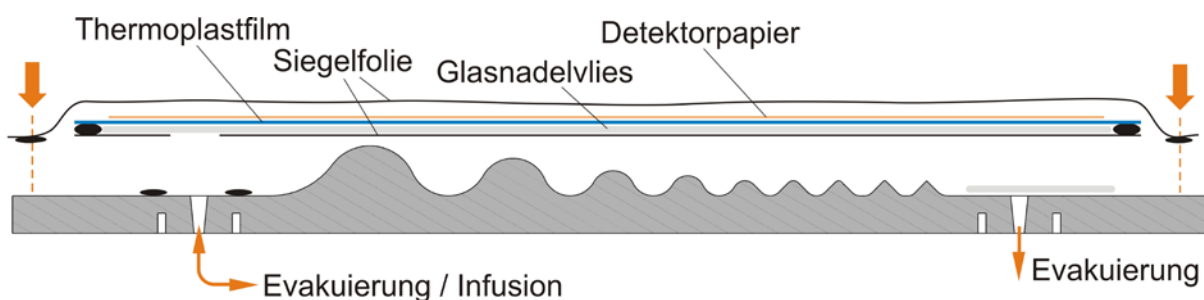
Prinzipieller Aufbau des Schikanenwerkzeugs mit dem infiltrierbaren Folienaufbau und der gemeinsamen Siegelfolie zur Anpassung des Folienaufbaus an die Werkzeugkontur
